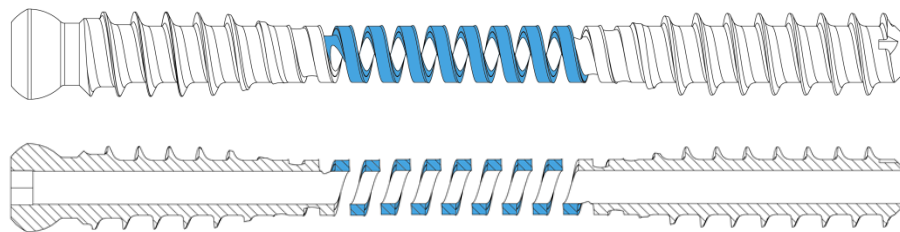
Chirurgische Schraube mit integrierter Federgeometrie
